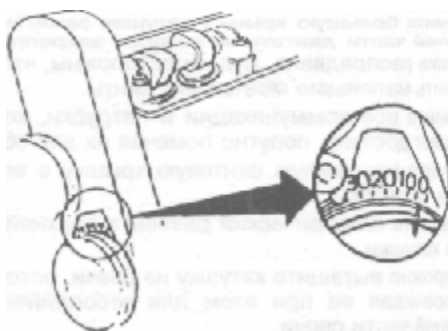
При регулировке зазоров клапанов риска угла зажигания на шкиве должна указывать на "O" - двигатели B230F и B230FT
